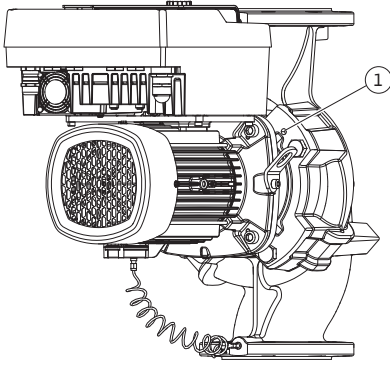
Abdrücken des Einstecksatzes über Gewindebohrungen
